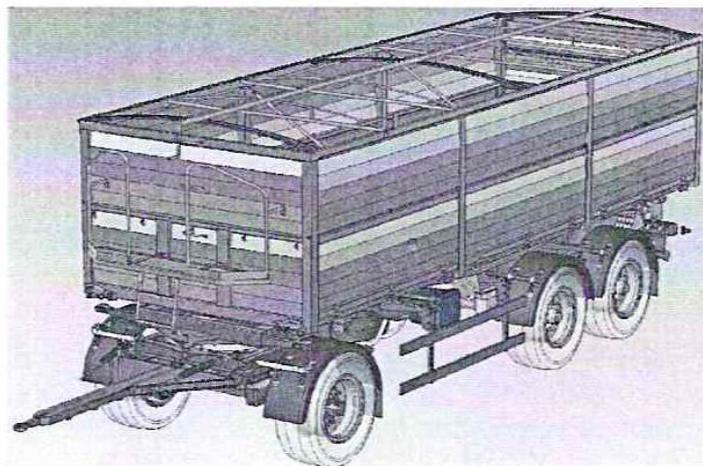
Прицеп самосвальный (зерновоз) трехосный с механическим запорным механизмом 7200
